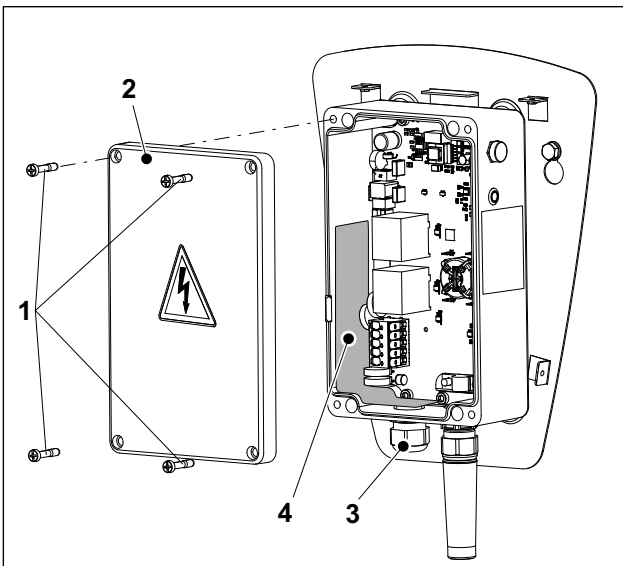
Heidelberg Wallbox Home Eco, caja del aparato electrónico abierta
